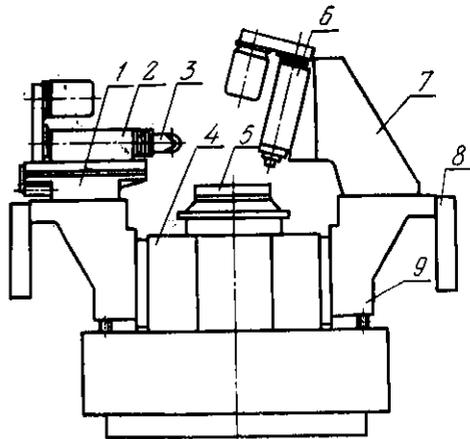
Схема компоновки малогабаритного агрегатного станка
